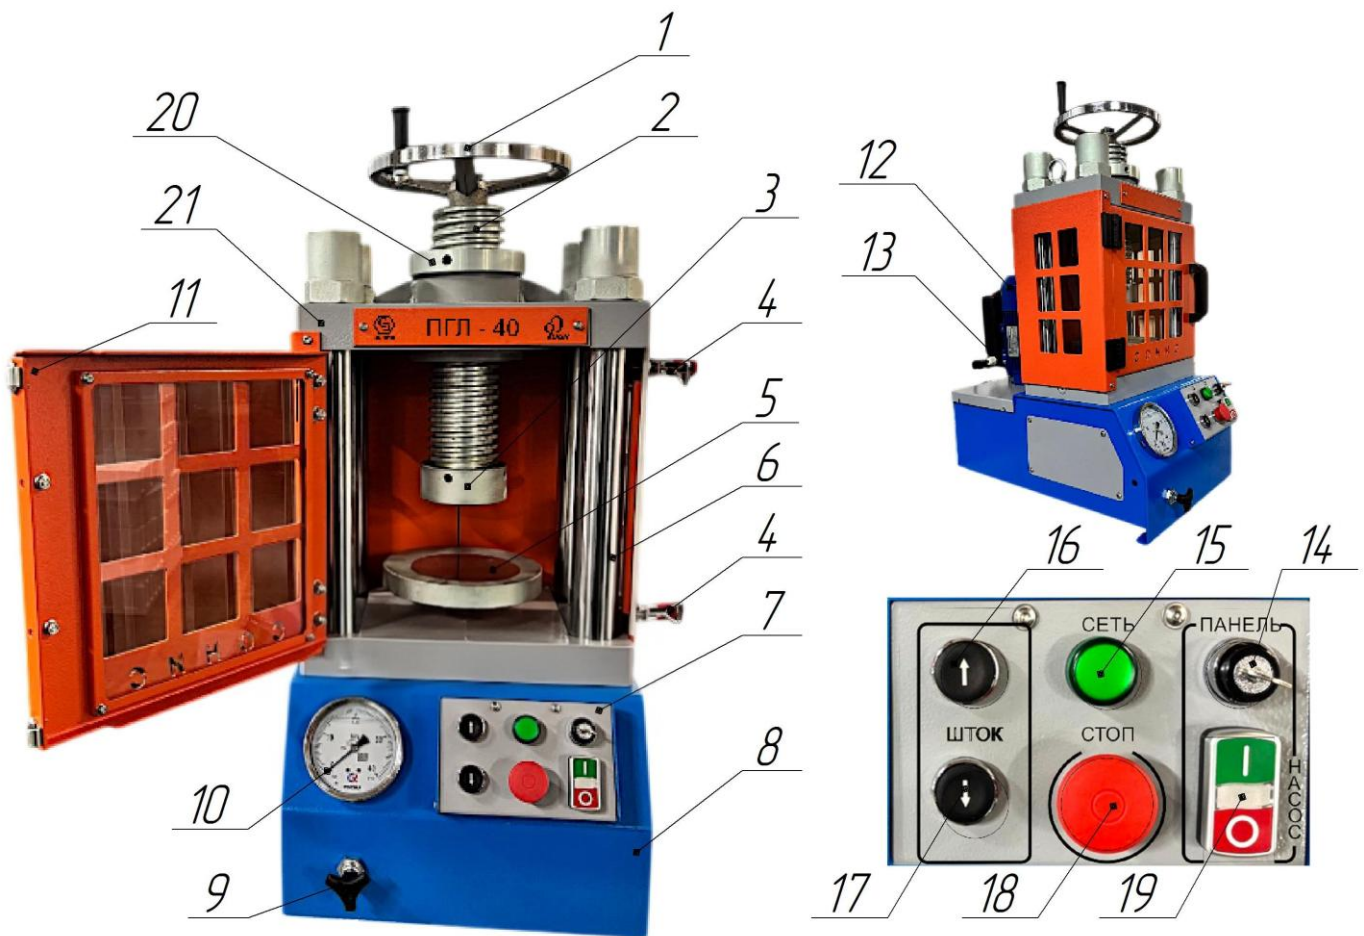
Общий вид пресса и его панели управления: 1 - штурвал; 2 - силовой винт; 3 - пята; 4 - защелки; 5 - опора; 6 - стойка; 7 - панель управления; 8 - корпус; 9 - регулятор давления; 10 - манометр; 11 - защитный экран; 12- электродвигатель; 13 - выключатель "сеть"; 14 - замок блокировки панели управления; 15 - индикатор "сеть"; 16 - кнопка штока "вверх"; 17 - кнопка штока "вниз"; 18 - кнопка "аварийный стоп"; 19 - кнопка "пуск-стоп насоса"; 20 - контргайка; 21 - траверса.
